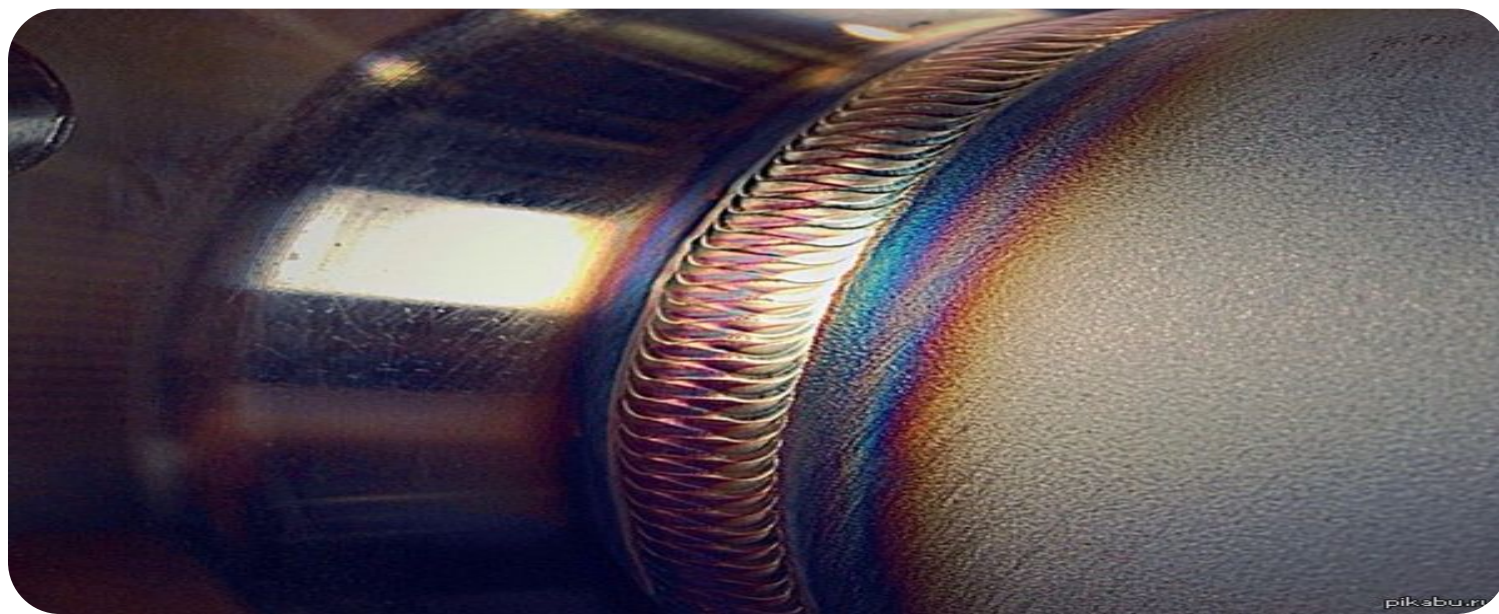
Сварное соединение: 1 – сварной шов; 2 – зона сплавления; 3 – зона термического влияния; 4 – основной металл.
